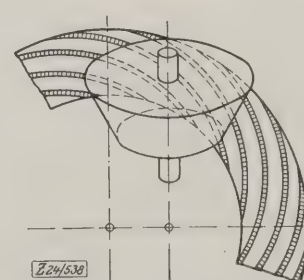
Scheibenschraube zur Erzeugung von Kegelrädern im reinen Schraubverfahren.
